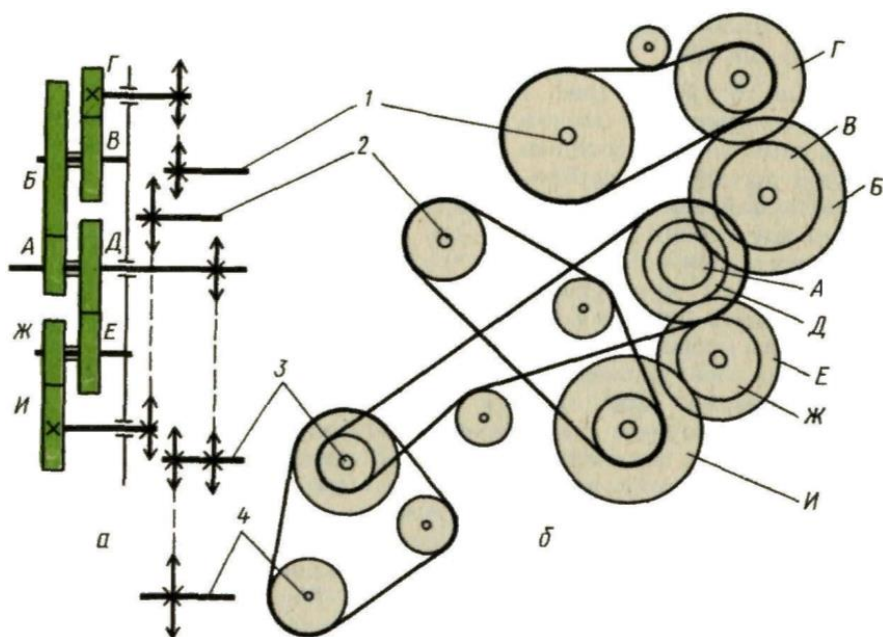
Рис. 13. Цепочно-зубчатый механизм привода сеялки СЗ-3,6:
